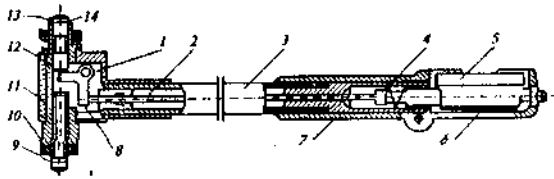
Конструкция индикаторного нутромера: 1 – ось вращения рычага; 2 – шток; 3 – трубка; 4 и 14 – пружина; 5 – отсчетное устройство (индикатор); 6 – предохранительный кожух; 7 – теплоизоляционная рукоятка; 8 – Г-образный рычаг; 9 – неподвижный (регулируемый) стержень; 10 – контргайка; 11 – корпус; 12 – шарик; 13 – подвижный измерительный стержень; 14 – риска
